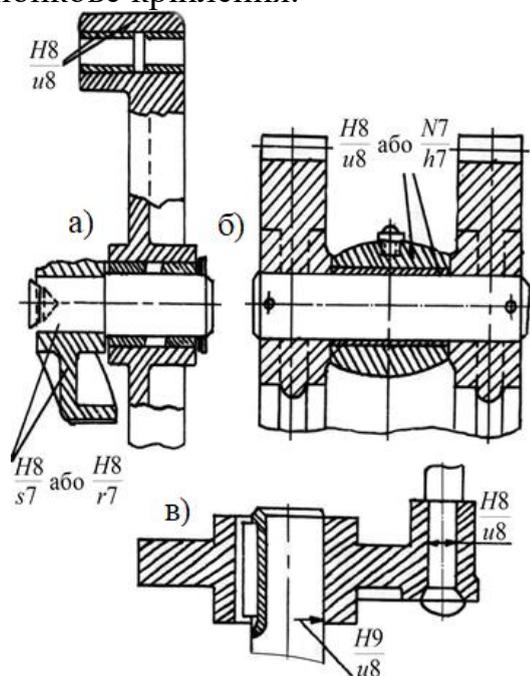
Приклади застосування посадок з натягом [2]: а) – важіль приводу зернозбирального комбайну; б) – кривошипні шестірні сінного преса; в) – кривошип косарки для косозубого
